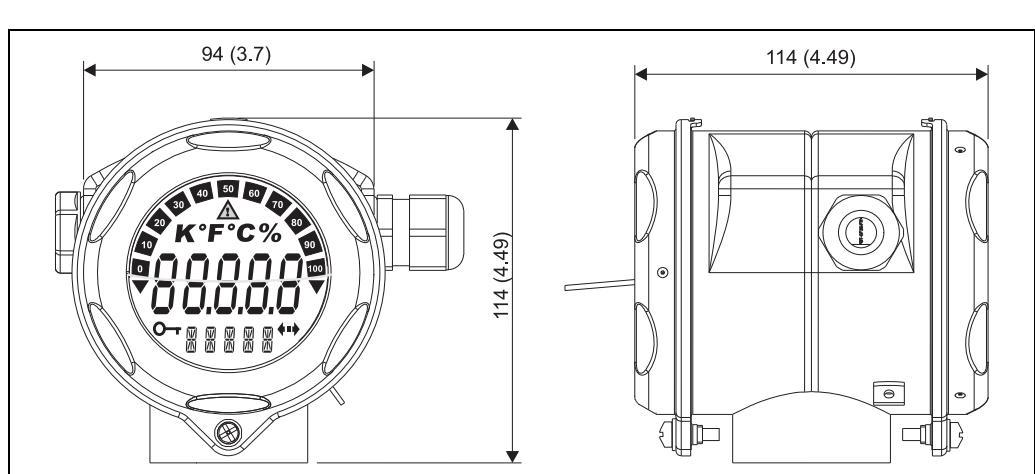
Литой под давлением алюминиевый корпус общего назначения или, по отдельному заказу, корпус из нержавеющей стали (316L)
